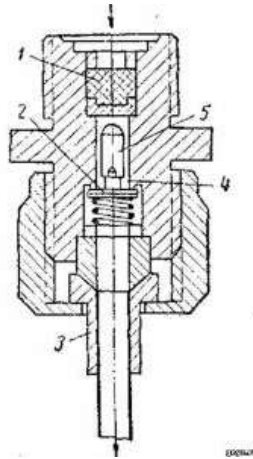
Дозирующий клапан для централизованной жидкой смазки.
